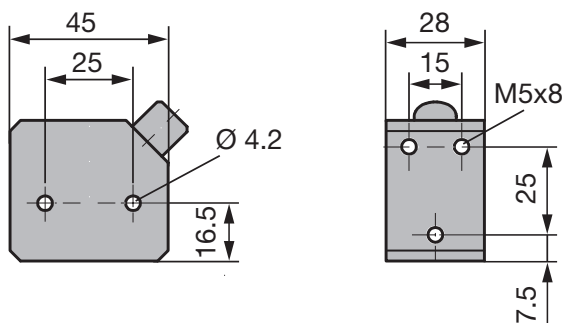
Dimensioni di ingombro datore di posizione BTL5-P-4500-1
